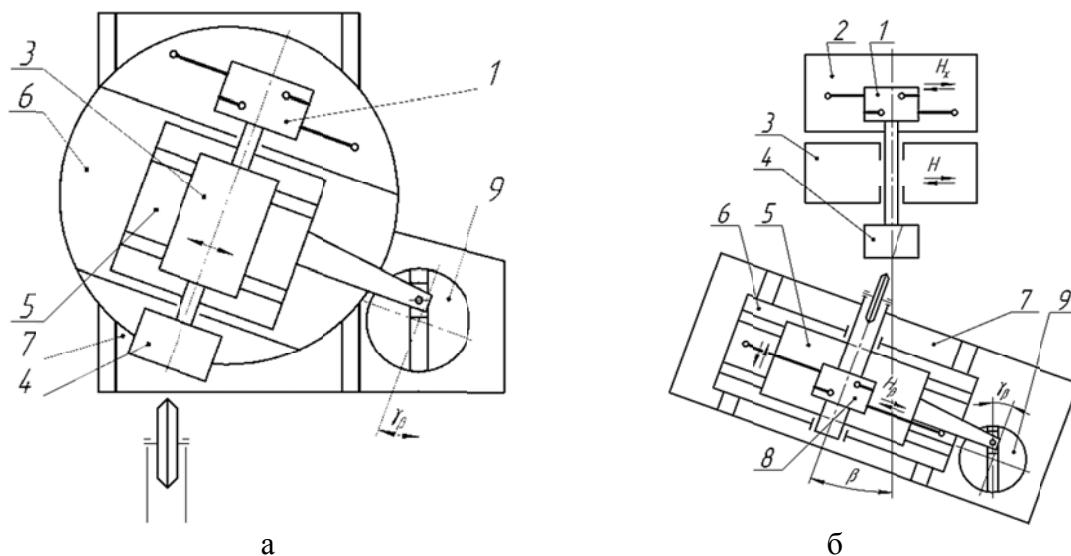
Схемы сокращения длины хода обкатки при шлифовании зубчатых колёс
